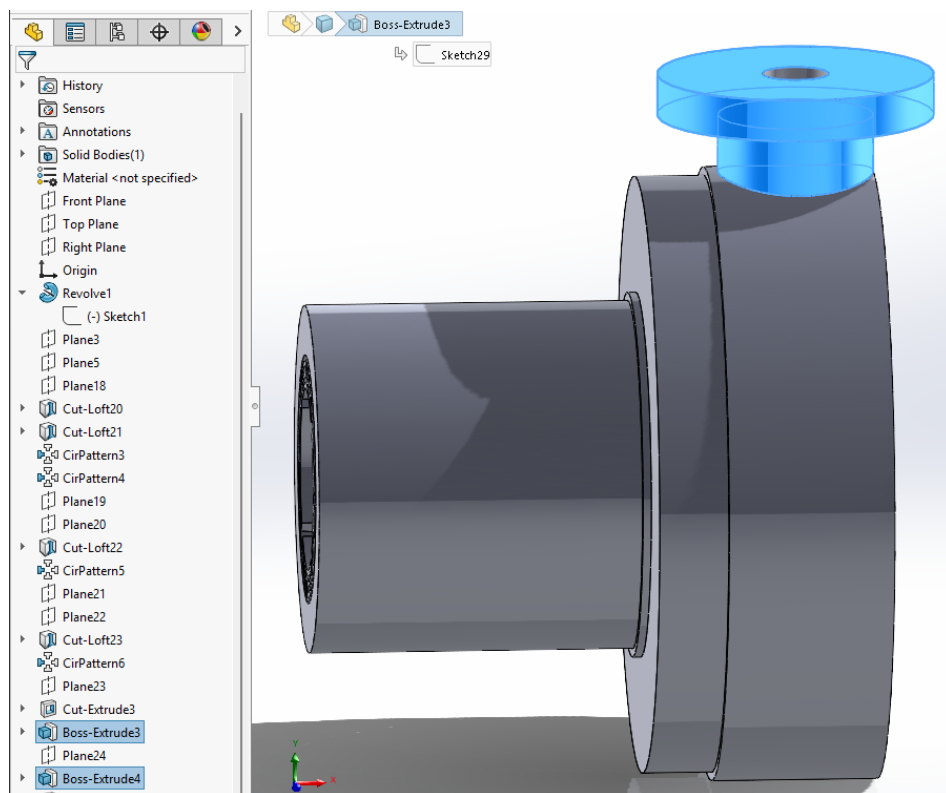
Корпус та фланець додаткового каналу, «Boss Extrude»
